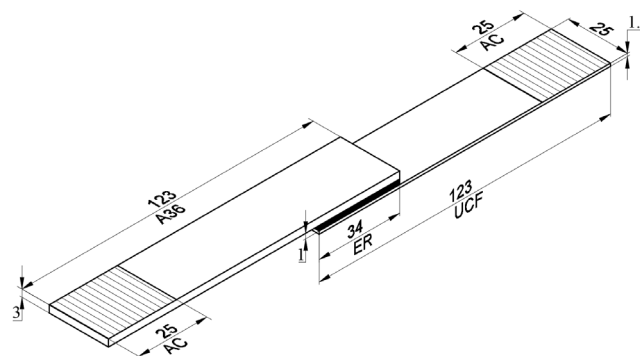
Dimensiones de las probetas. AC: área para sujetar en las mordazas de la máquina de ensayos; ER: resina epóxica; UCF: fibra de carbono unidireccional; A36: acero ASTM A36.
